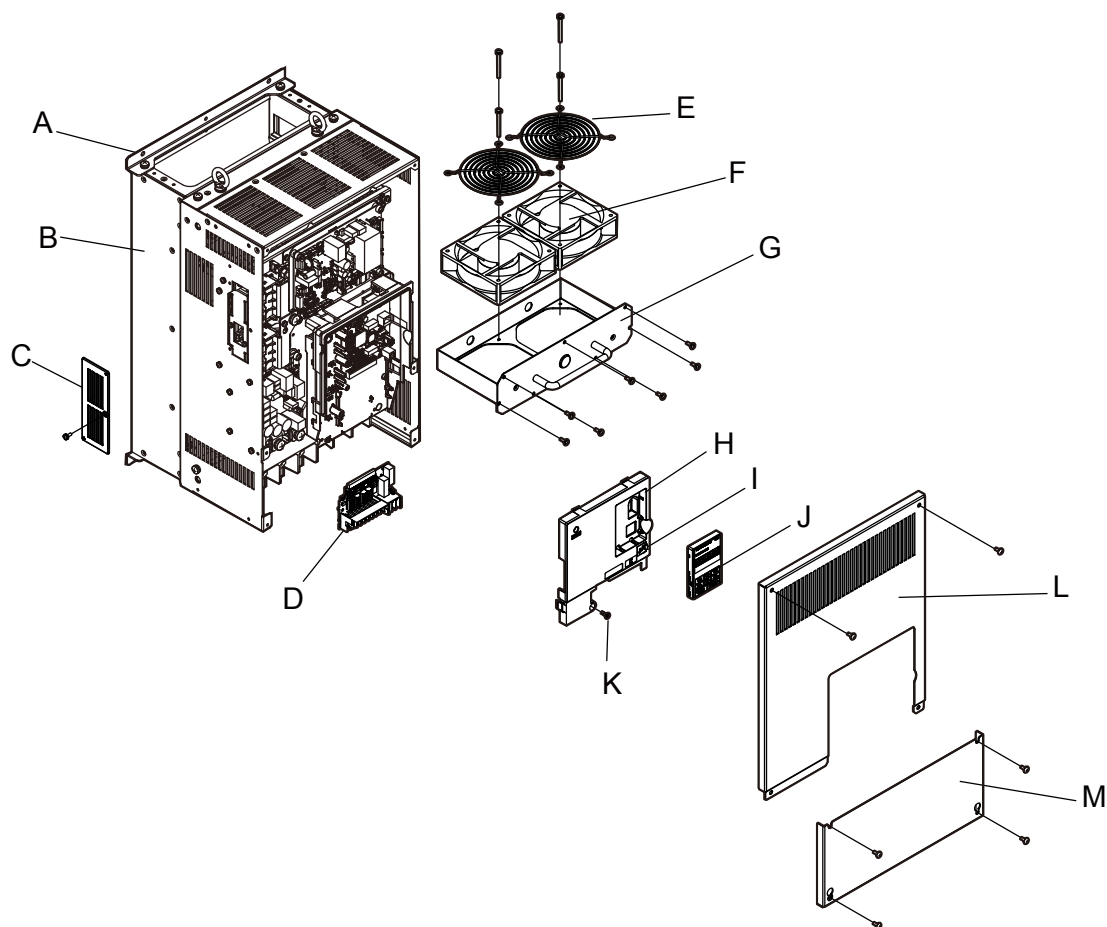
Vista explodida dos componentes de gabinete do tipo 1 IP20/NEMA (CIMR-A□4A0165F)
